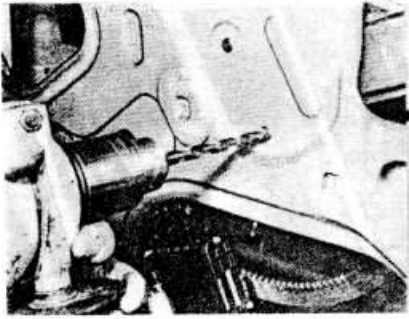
Высверливание заклепки крепления стеклоподъемника передней двери
